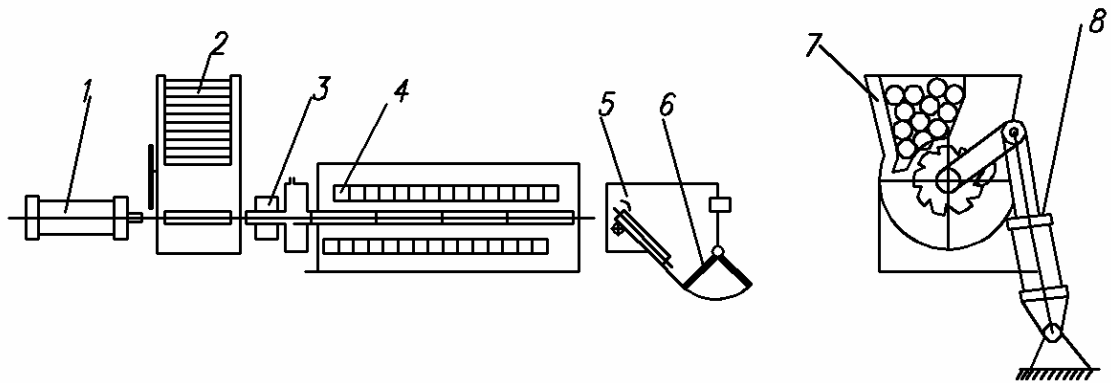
Нагреватель для безокислительного нагрева заготовок в защитной атмосфере
